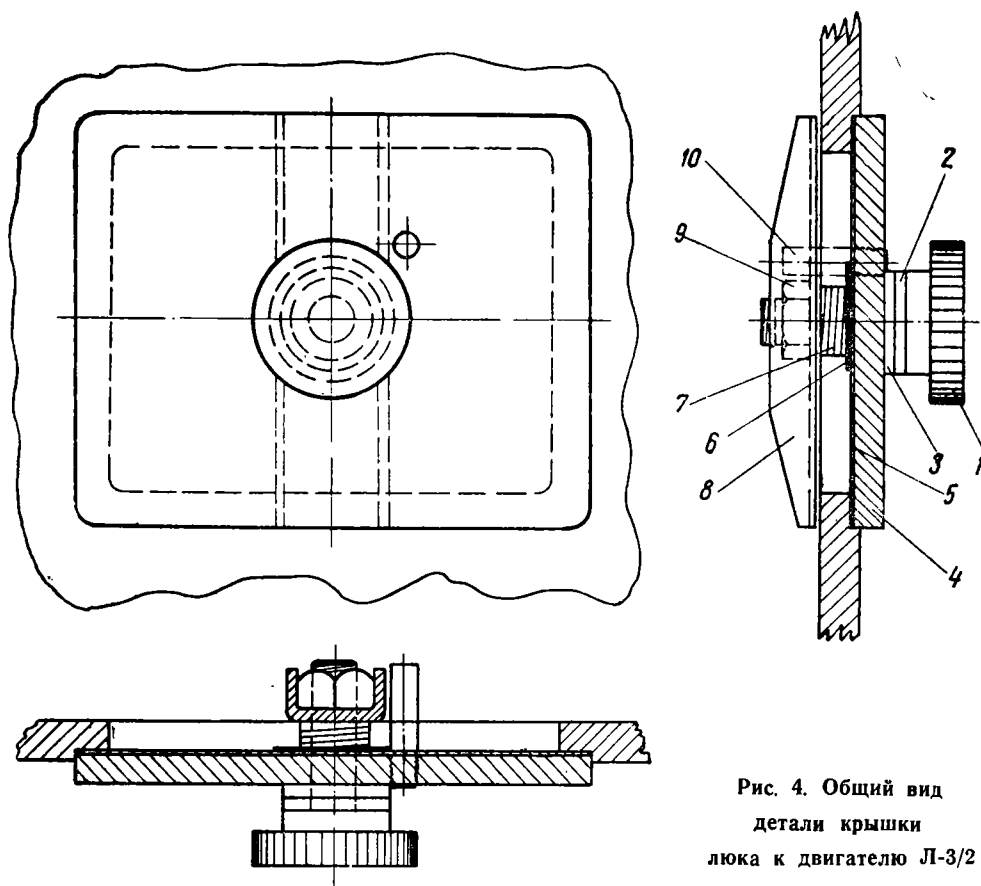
Общий вид детали крышки люка к двигателю Л-3/2
